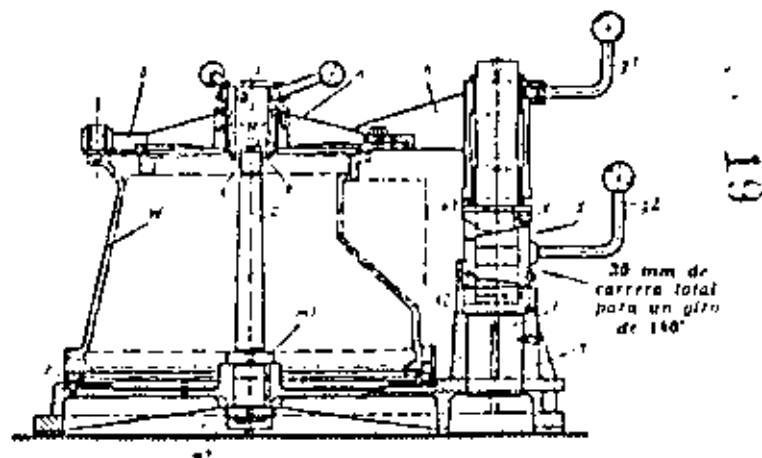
Dispositivo de taladrado con dispositivos de levantamiento y giro para la placa de taladrar.
